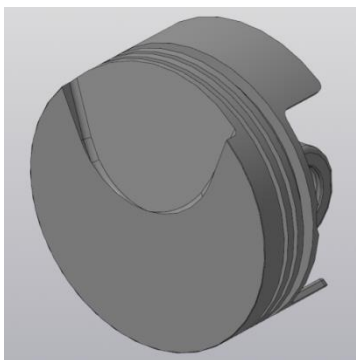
Поршень ПДП-двигателя с «боковой клиновидной вихревой» камерой.
